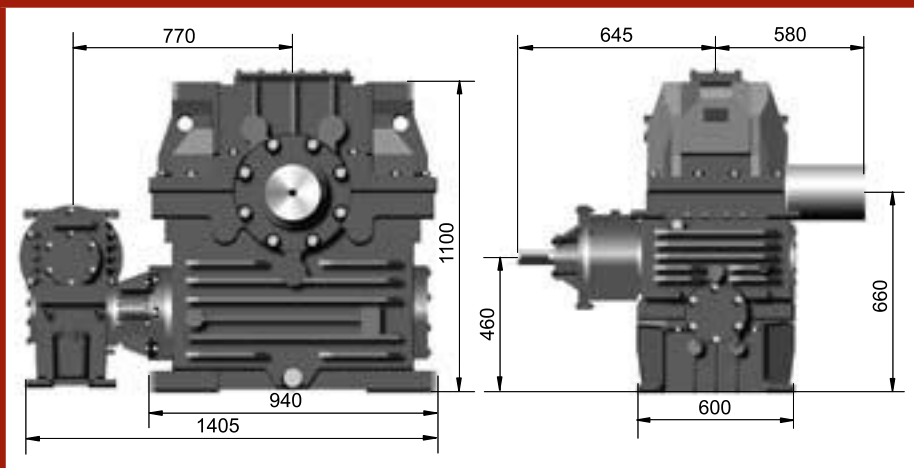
Габаритные размеры редуктора ПЧ2-200/400М
